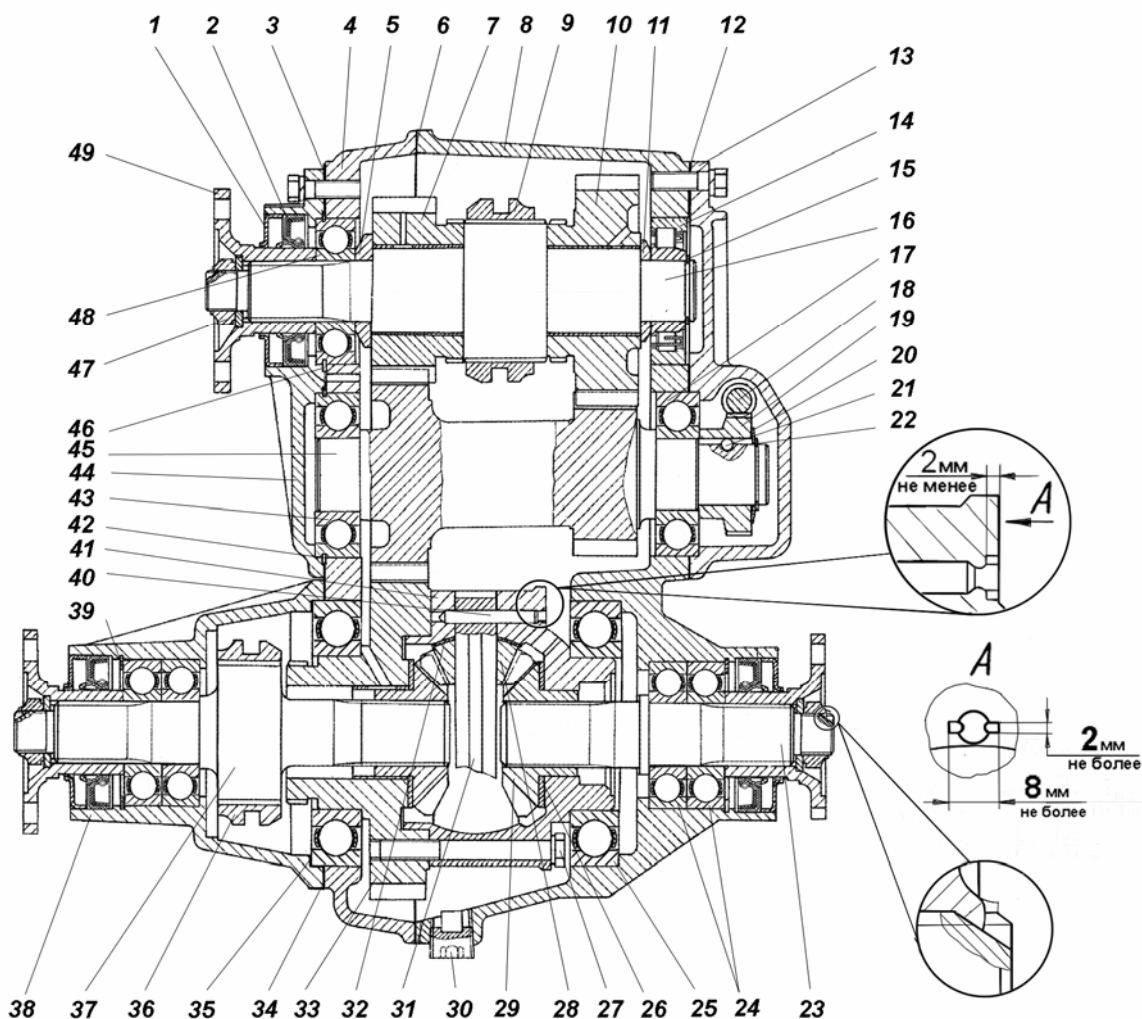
Раздаточная коробка: 1 – защитное кольцо; 2 – манжета; 3,6,12,34 – прокладки; 4 – передний картер; 5,11 – упорные шайбы; 7 – шестерня понижающей передачи; 8 – задний картер; 9 – муфта переключения передач; 10 – шестерня высшей передачи; 13 – задняя крышка; 14 – задний подшипник первичного вала; 15,22,39,42,46 – стопорные кольца; 16 – первичный вал; 17 – задний подшипник промежуточного вала; 18 – шестерня ведомая привода спидометра; 19 – шестерня ведущая привода спидометра; 20 – пружинная шайба; 21 – шарик фиксирующий; 23 – вал привода заднего моста; 24 – подшипники; 25 – подшипник дифференциала; 26 – опорная шайба шестерни полуоси; 27 – болт; 28 – сателлит; 29 – шестерня полуоси; 30 – пробка сливного отверстия; 31 – ось сателлитов; 32 – опорная шайба сателлита; 33 – шестерня дифференциала; 35 – регулировочные прокладки; 36 – муфта включения блокировки дифференциала; 37 – вал привода переднего моста; 38 – крышка механизма управления; 40 – стопор оси; 41 – коробка сателлитов дифференциала; 43 – подшипник передний промежуточного вала; 44 – передняя крышка; 45 – промежуточный вал; 47 – гайка; 48 – подшипник передний первичного вала; 49 – фланец
